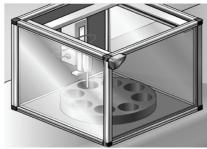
Protección de punto peligroso con un sistema SC300 montado sobre la estructura
